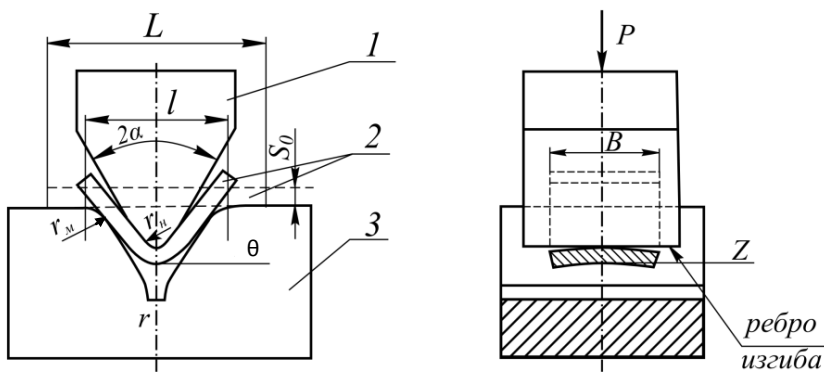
Схема поперечного изгиба в листовой заготовке в штампе:
